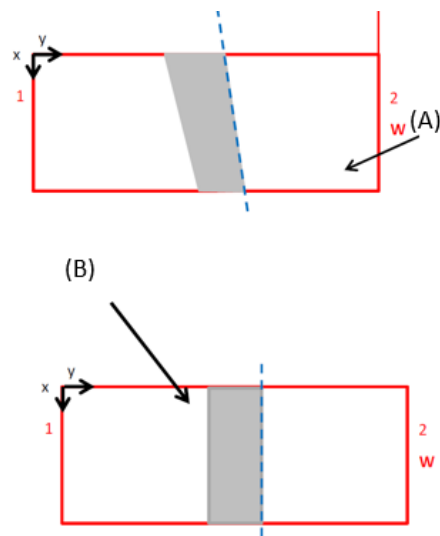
Relación entre direcciones de mecanización de probetas y cordón de soldadura.
